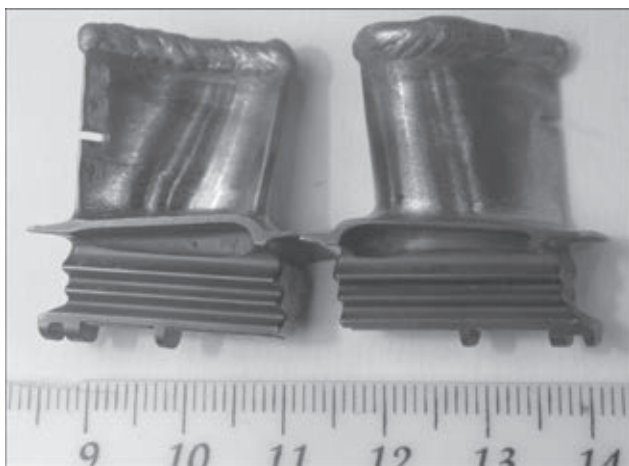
Лопатки после восстановления торца пера (основной и наплавленный металл — сплав ЖС32)
